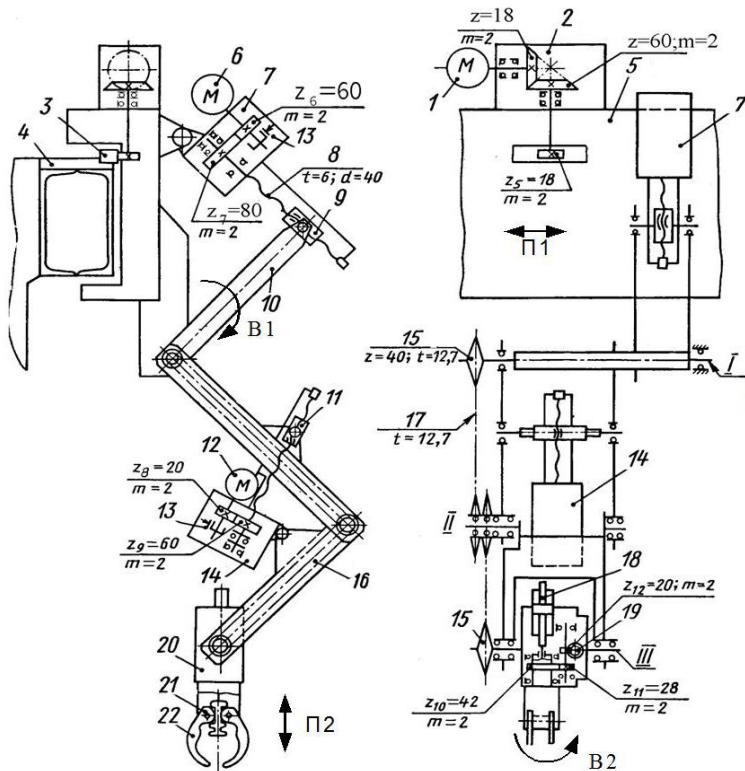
Промышленный робот: 1 – гидромотор; 2 – редуктор; 3 – шестерня-рейка; 4, 5 – портал; 6 – гидромотор; 7 – редуктор; 8 – винт; 9 – гайка; 10 – плечо ПР; 11 – передача винт-гайка; 12 – гидромотор; 13 – тормоз; 14 – редуктор; 15, 17 – цепные передачи; 16 – локоть ПР; 18 – гидроцилиндр схвата; 19 – гидромеханическое устройство поворота схвата; 20-22 – схват ПР
